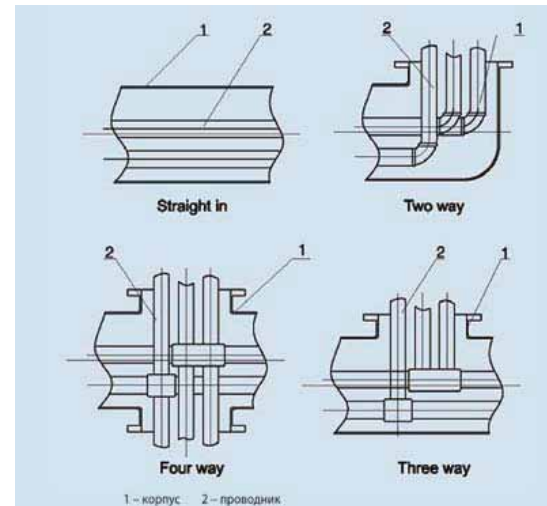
Схема конструкции трехфазной шины с отводами обычного барабанного типа
